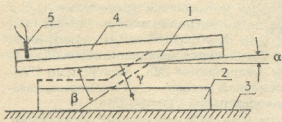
Схема сварки взрывом: 1 - μεταемая пластина - сталь 08Х25Г15С; 2 - основной металл - Ст. 3; 3 - опора; 4 - взрывчатое вещество; 5 - детонатор
